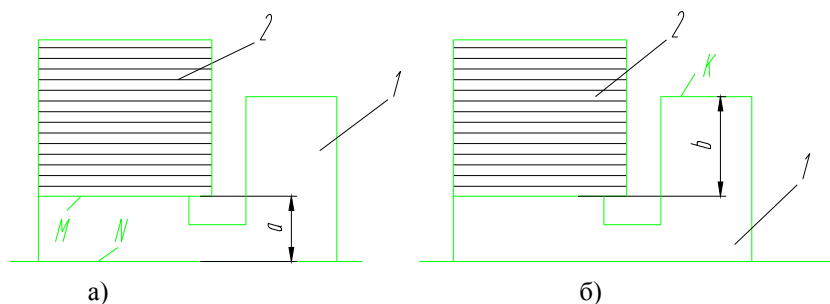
Фрезерование плоскости (1 - заготовка; 2 - фреза).
